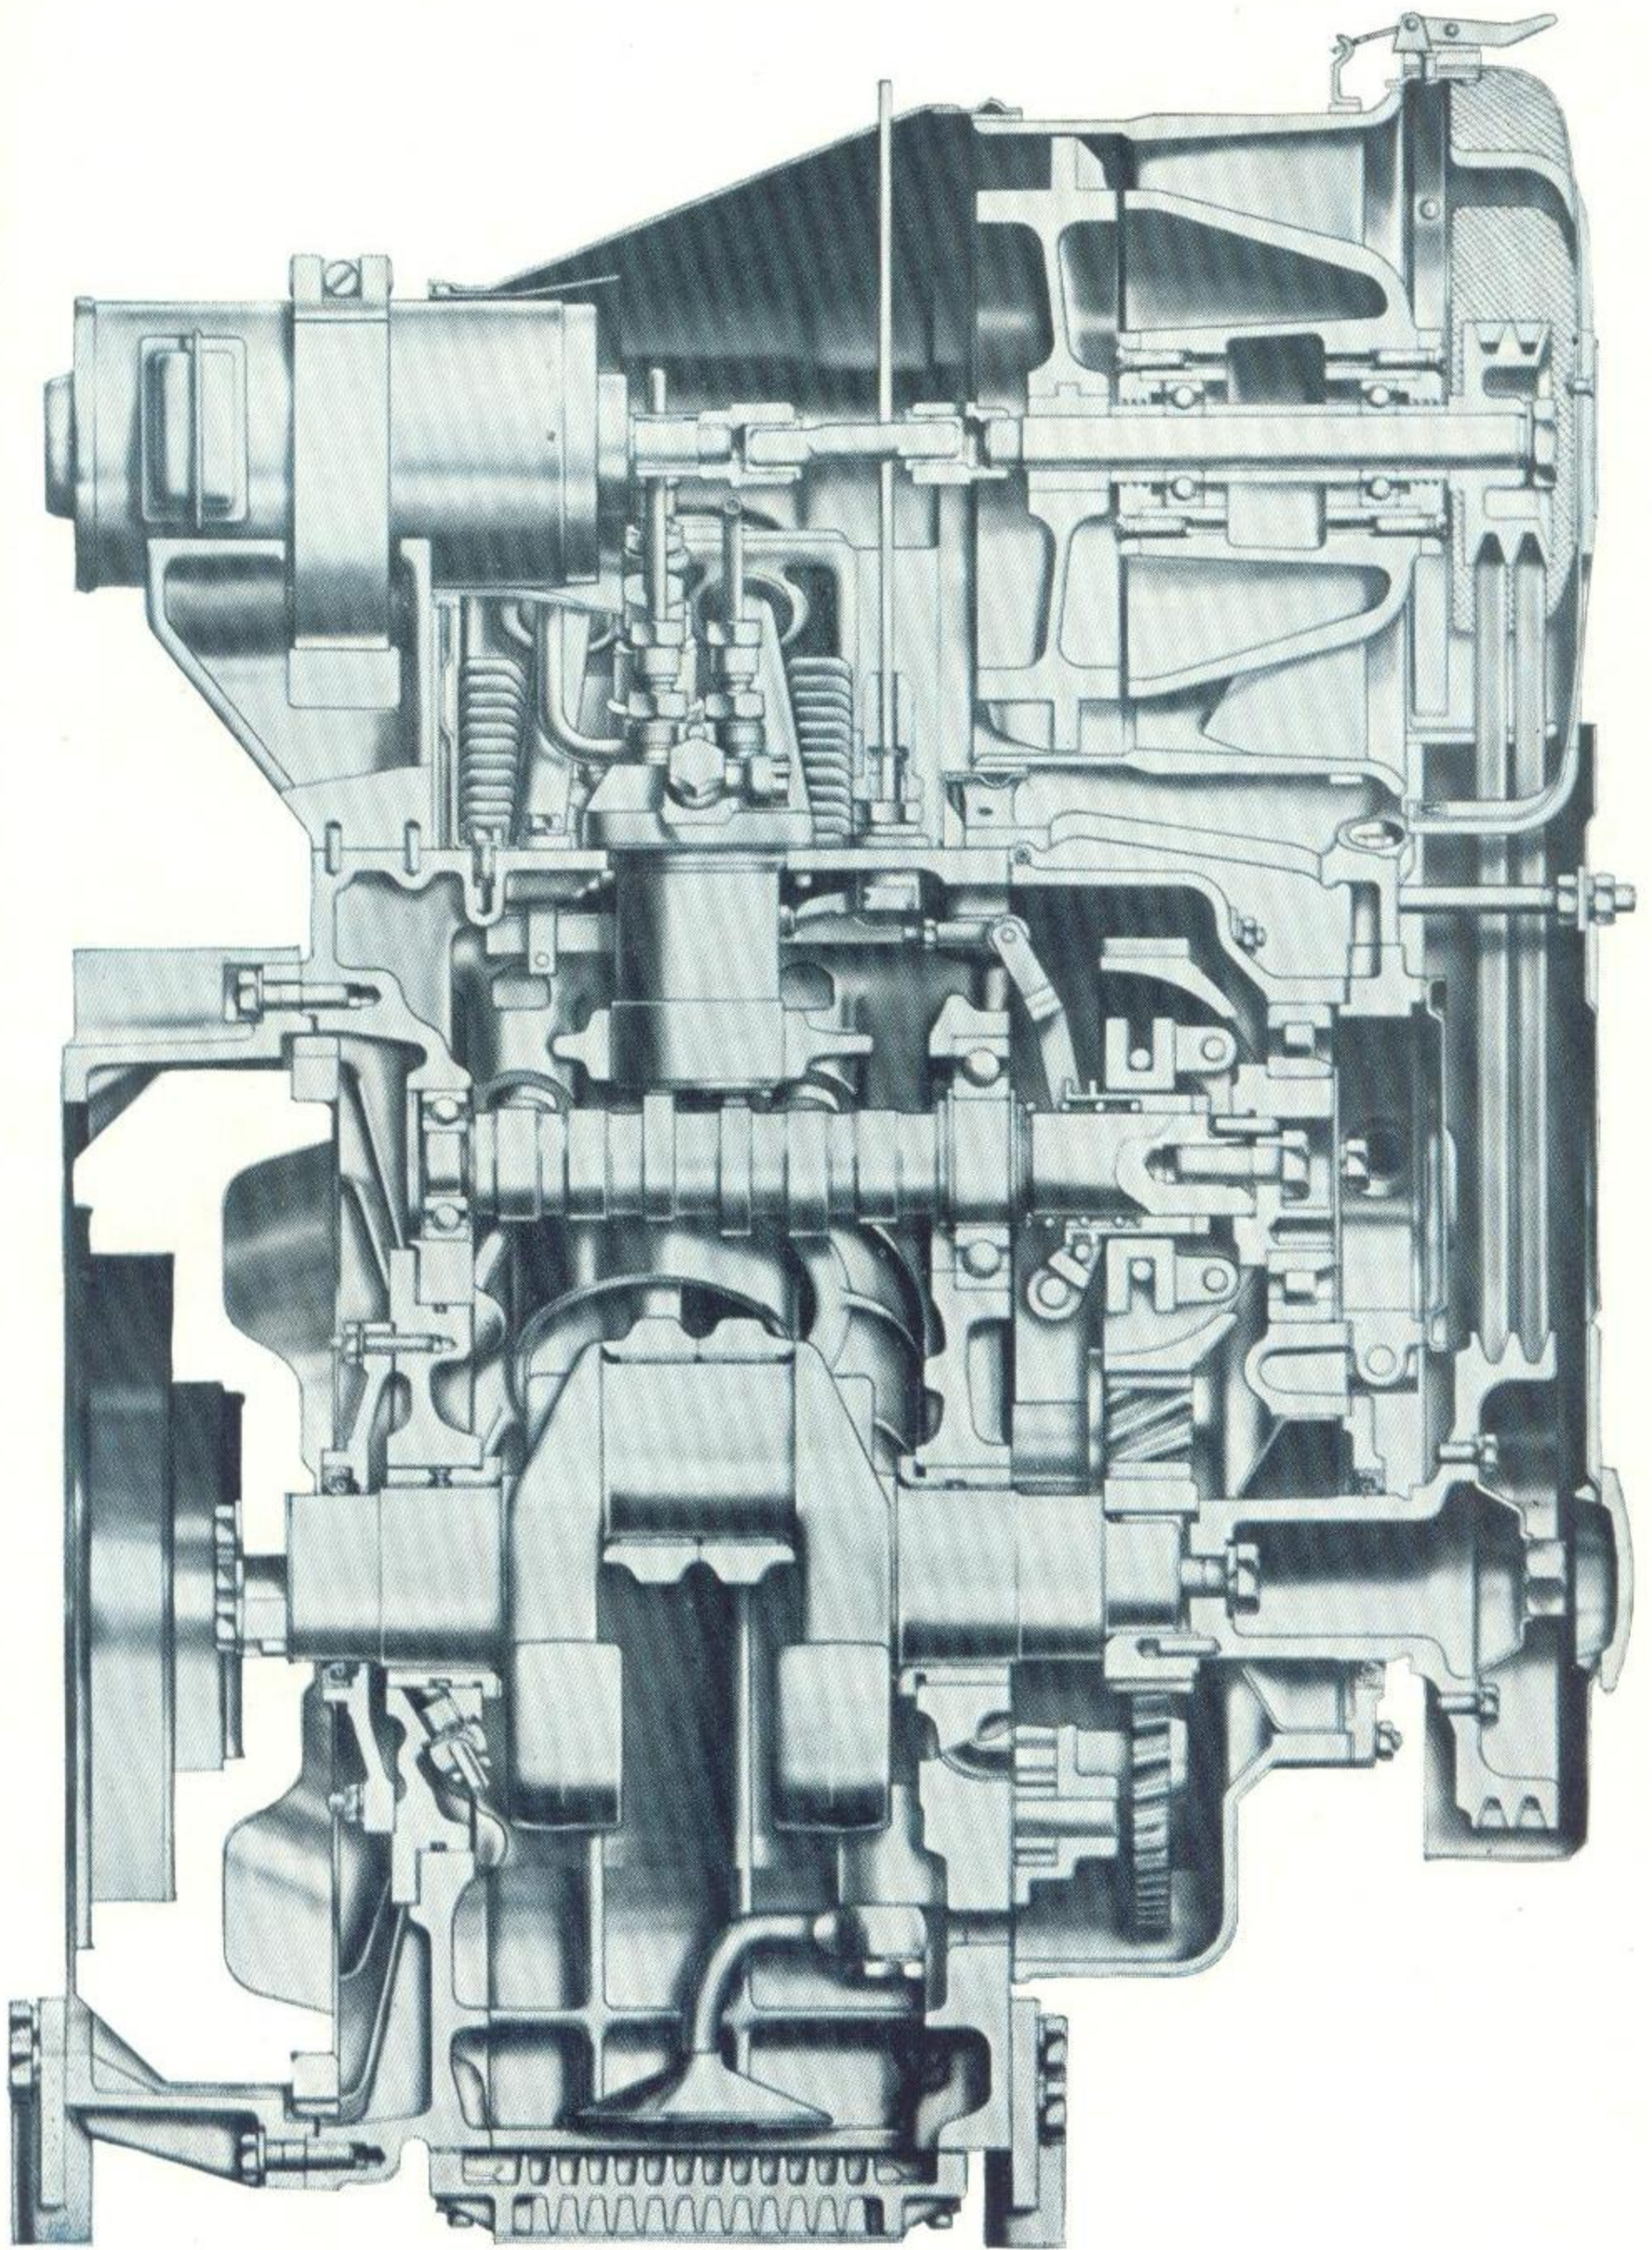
Motor 1 KVD 8 SL, podélný řez
